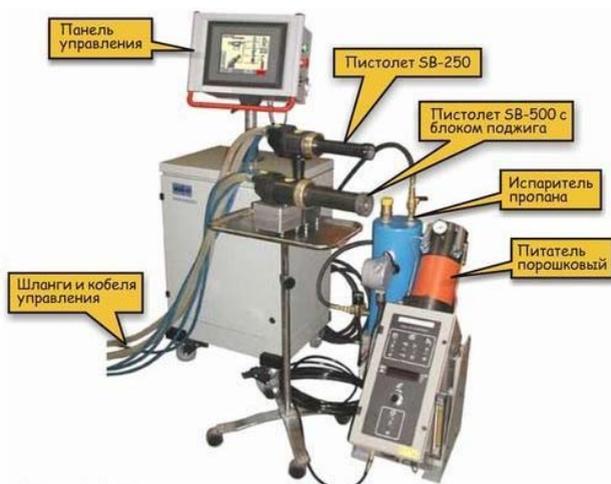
Установка для сверхзвукового газоздушного напыления порошков
